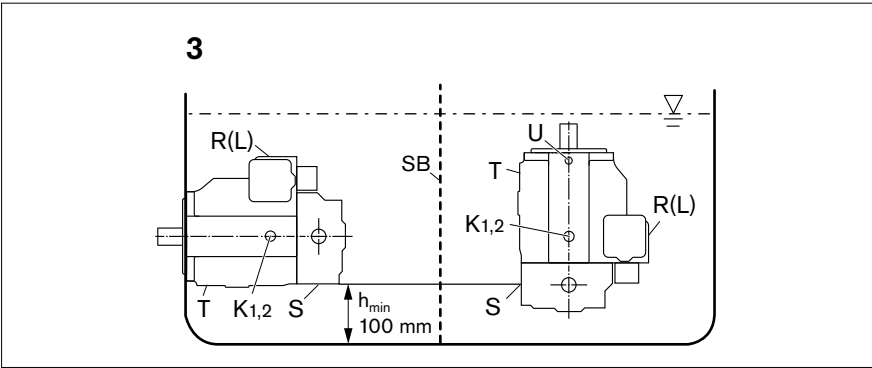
Tankeinbau mit waagrecht und senkrechter Einbaulage 3
